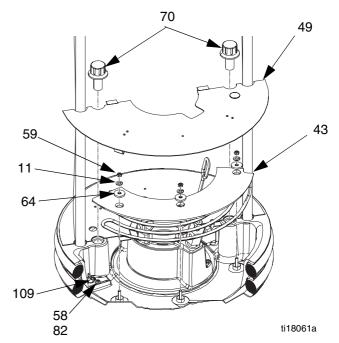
Remplacement des réchauffeurs de cylindre et du capteur de RTD
